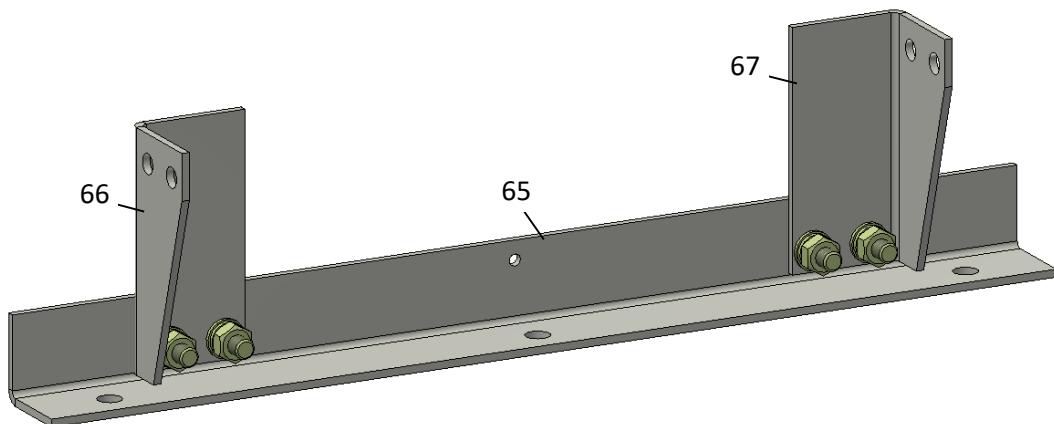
Сборка узла под верхние опорные изоляторы для ВЭ с ВМП-10К или ВМП-10П
